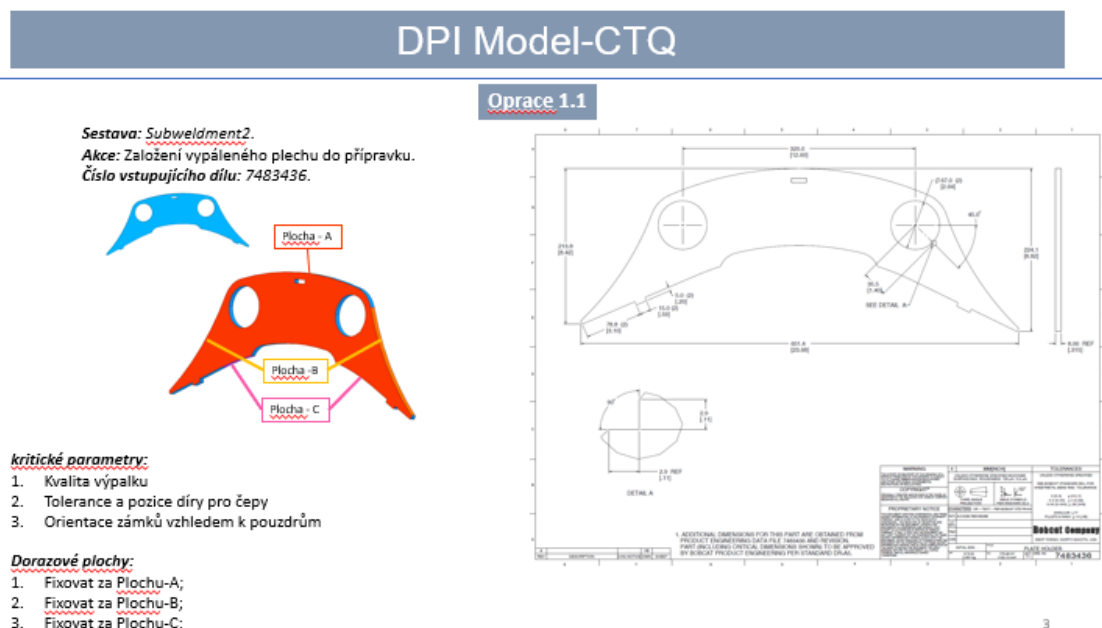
Vyznačené CTQ tolerance výložníku
